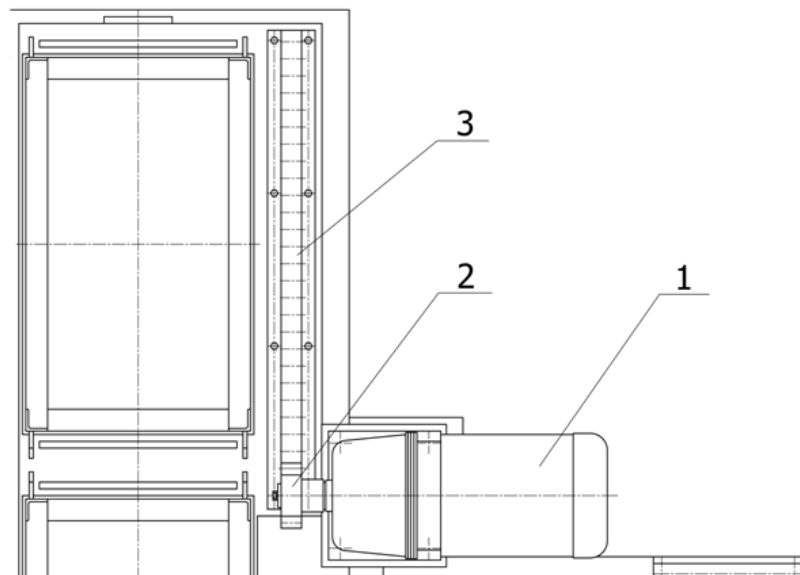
Привод перемещения каретки: 1 – мотор-редуктор; 2 – шестерня; 3 – рейка
